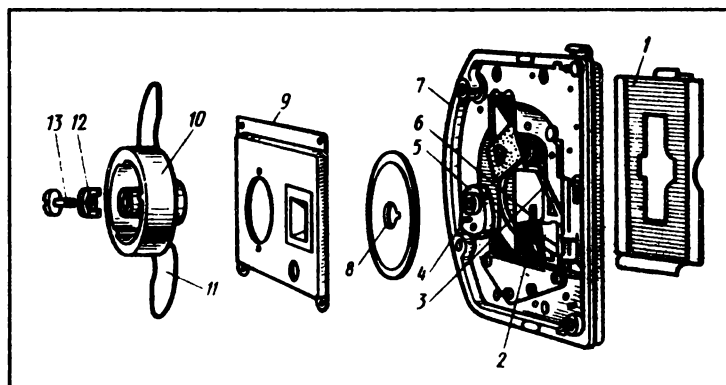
Корпус грейферного механизма (разобранный) кинопроектора П16П1:
